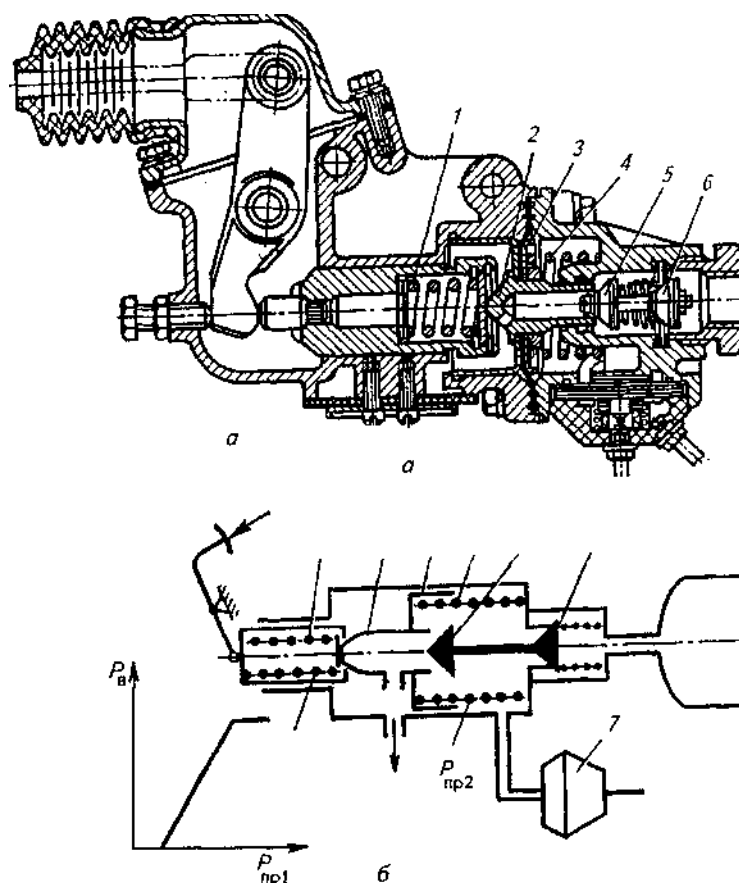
Тормозной кран прямого действия: а — конструкция; б — схема и статическая характеристика; 1, 4 — пружины; 2 — полый шток; 3 — поршень; 5 — атмосферный клапан; 6 — клапан сжатого воздуха; 7 — тормозная камера
